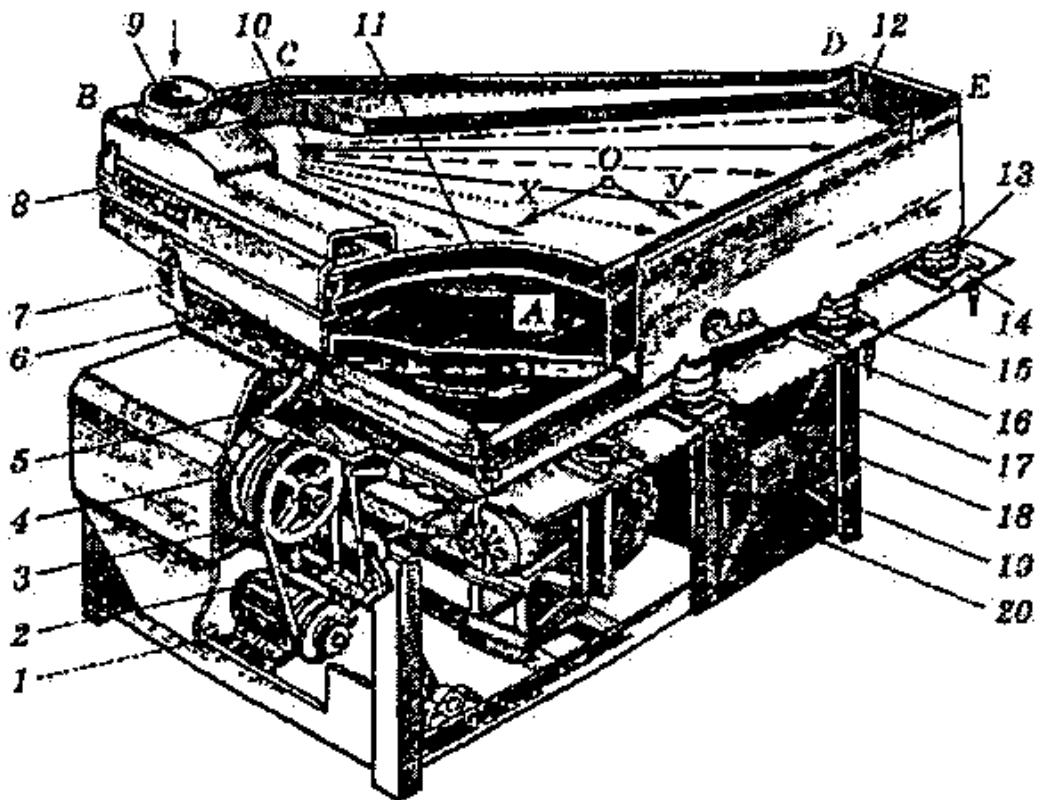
Пневматичний сортувальний стіл ПСС-2,5В:
